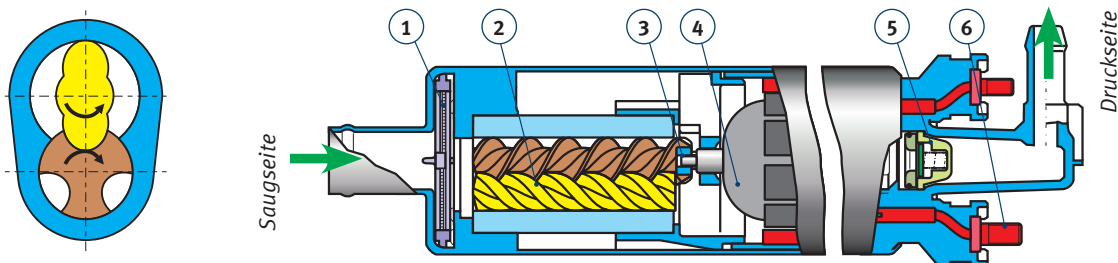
Pumpenprinzip und Schnitt (schematisch) durch eine Schraubenpumpe
